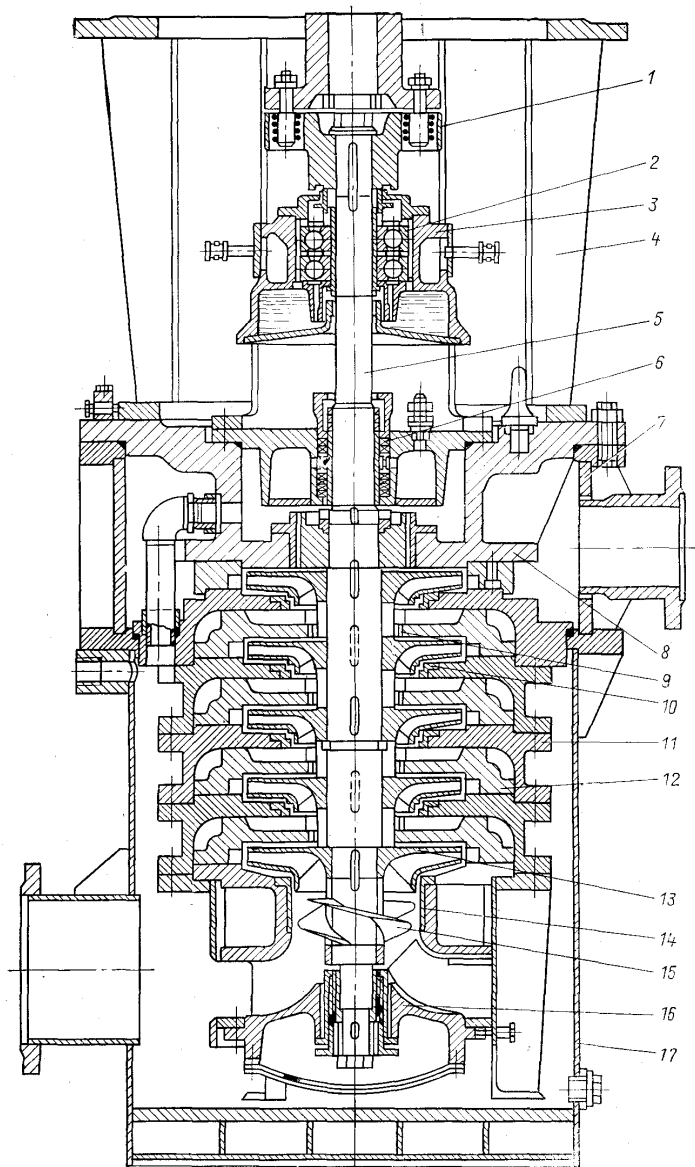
Конденсатный насос: 1 – муфта; 2 – опорно-упорный подшипник; 3 – корпус подшипника; 4 – фланец; 5 – вал; 6 – сальниковое уплотнение; 7 – напорный патрубок; 8 – напорная крышка; 9 – кольцо межступенчатого уплотнения; 10 – кольцо переднего уплотнения колеса; 11 – секция; 12 – аппарат направляющий; 13 – рабочее колесо; 14 – подвод; 15 – предвключенное колесо; 16 – опорный подшипник; 17 – наружный корпус
